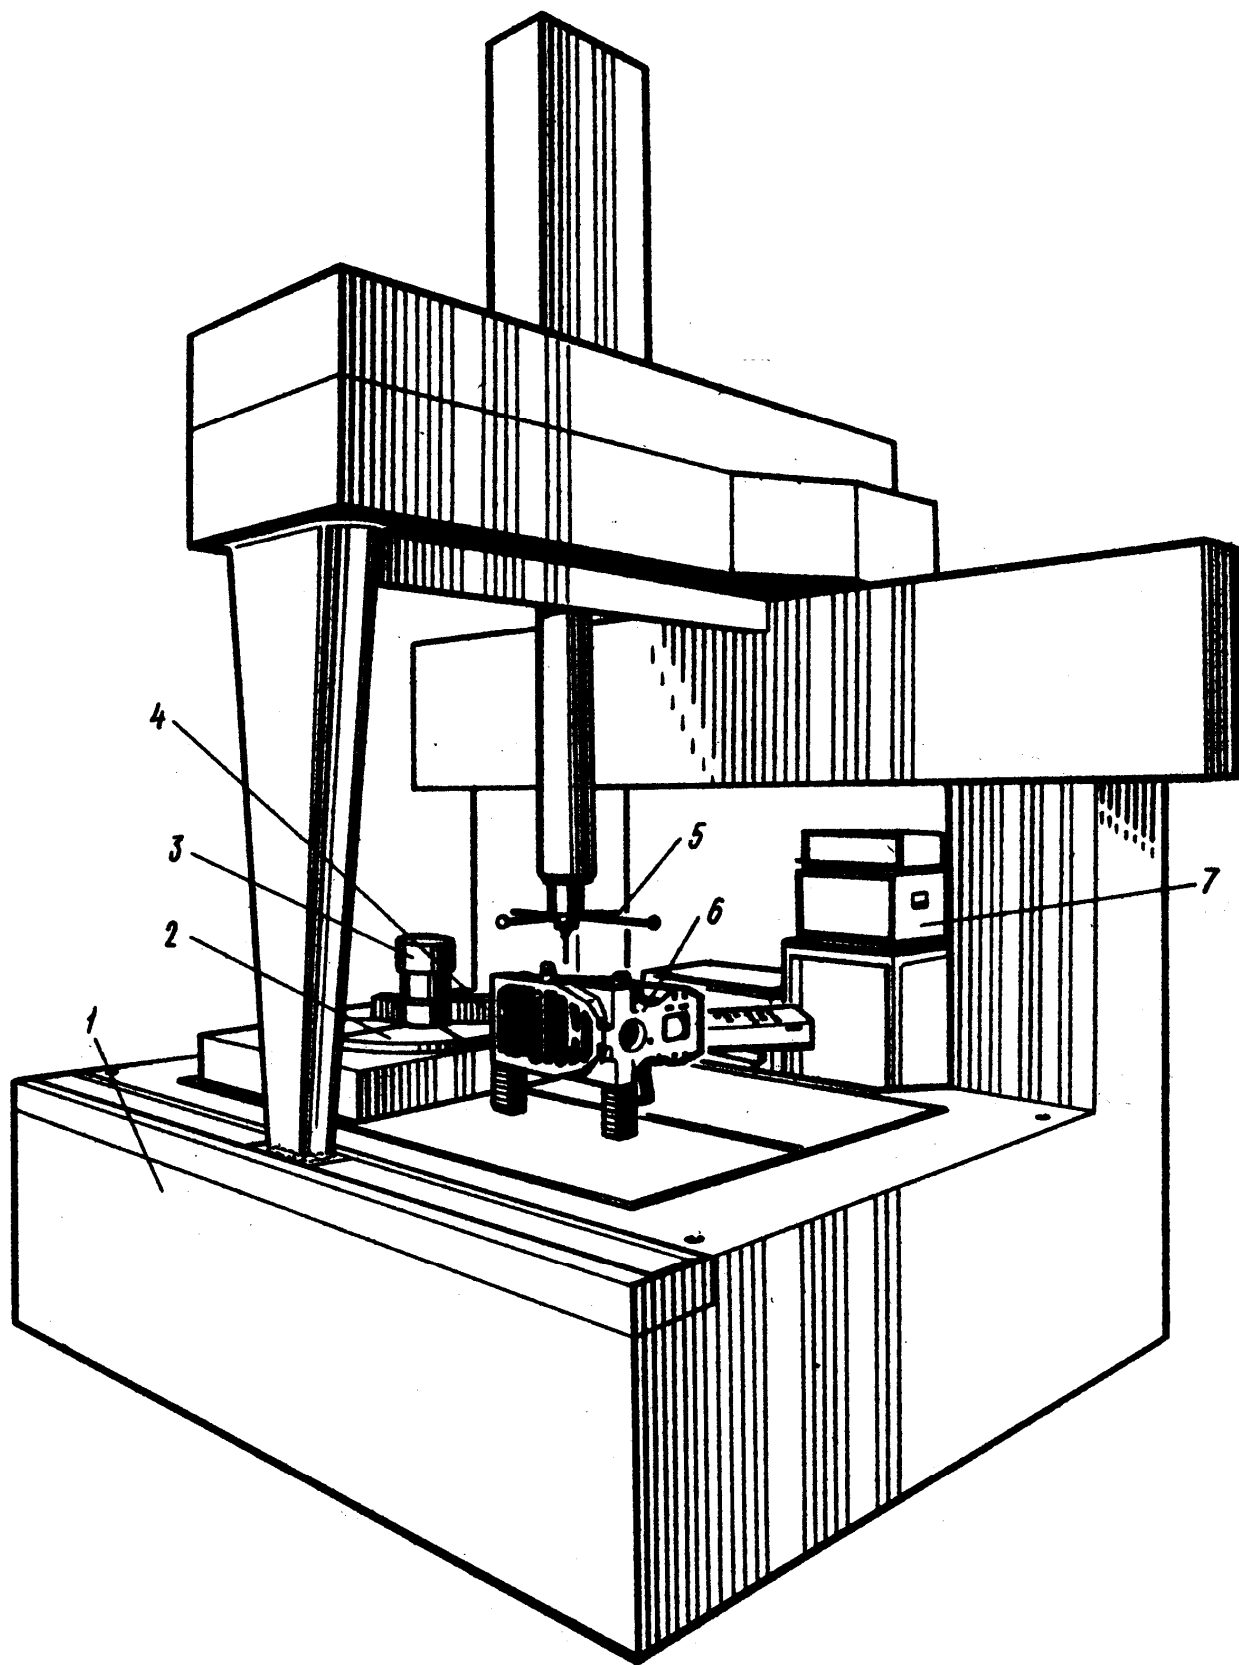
Загальний вигляд КІМ портального типу: 1 – корпус; 2 – поворотний стіл; 3 – притискний пристрій; 4 – деталь, яка очікує черги обслуговування; 5 – вимірювальні щупи; 6 – вимірювана деталь; 7 – система керування
